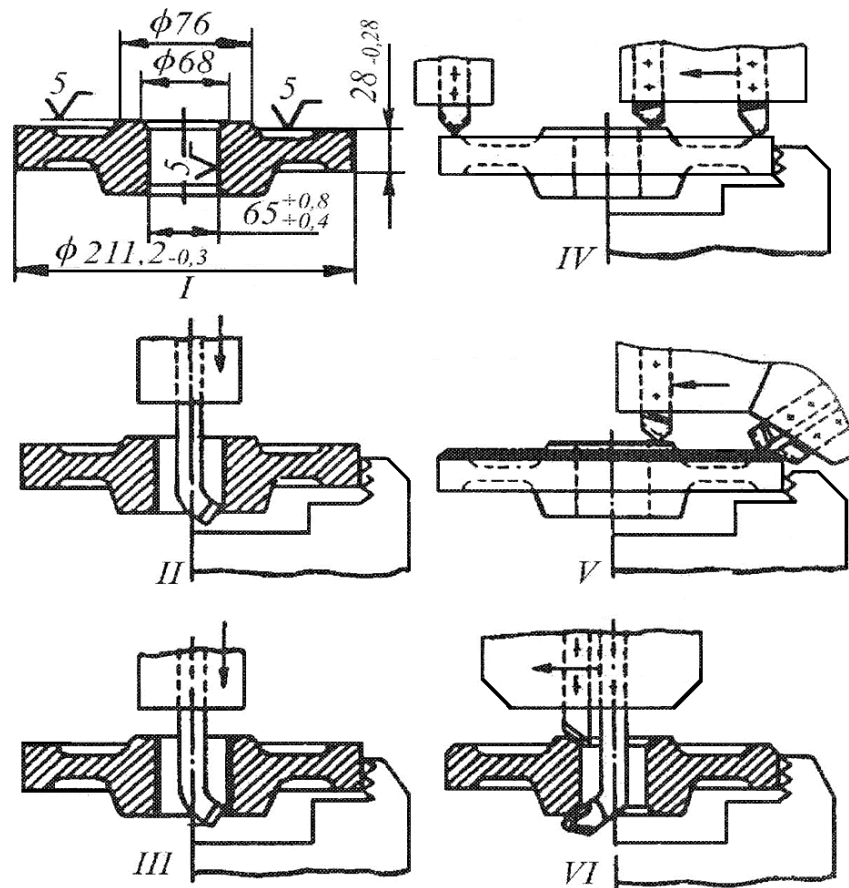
Схема налагодження вертикального шестишпindelного напівавтомата для виготовлення заготовки шестерні
